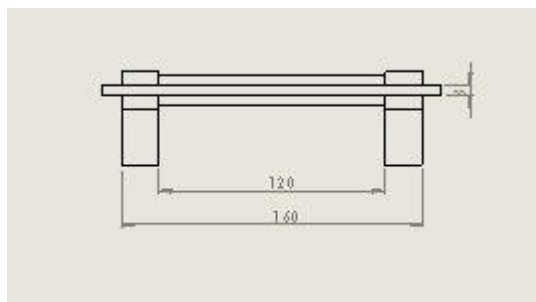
Desain 3 Dimensi Rancangan *Pokayoke Hole Lower B
